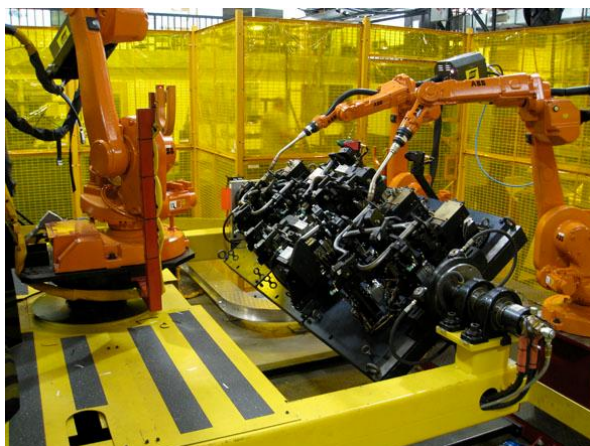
Célula de soldadura robotizada ABB com 3 robôs
